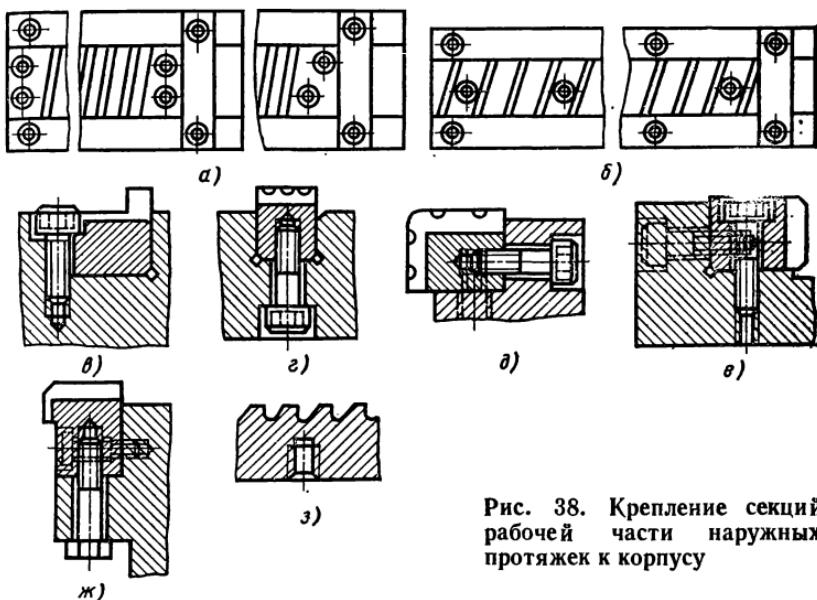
Крепление рабочей части наружных протяжек к корпусу
